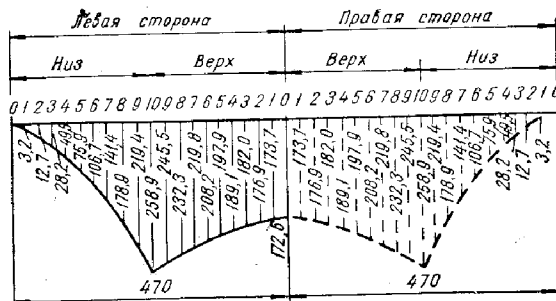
Развертка конца отрезка сварного тройника.
